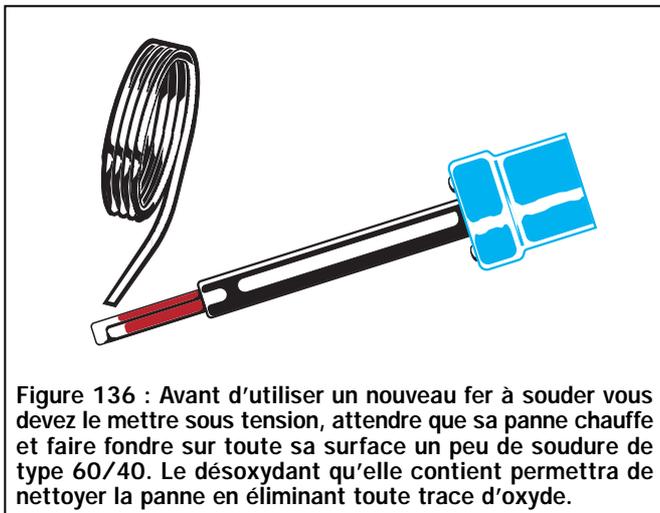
Avant d'utiliser un nouveau fer à souder vous devez le mettre sous tension, attendre que sa panne chauffe et faire fondre sur toute sa surface un peu de soudure de type 60/40. Le désoxydant qu'elle contient permettra de nettoyer la panne en éliminant toute trace d'oxyde.
